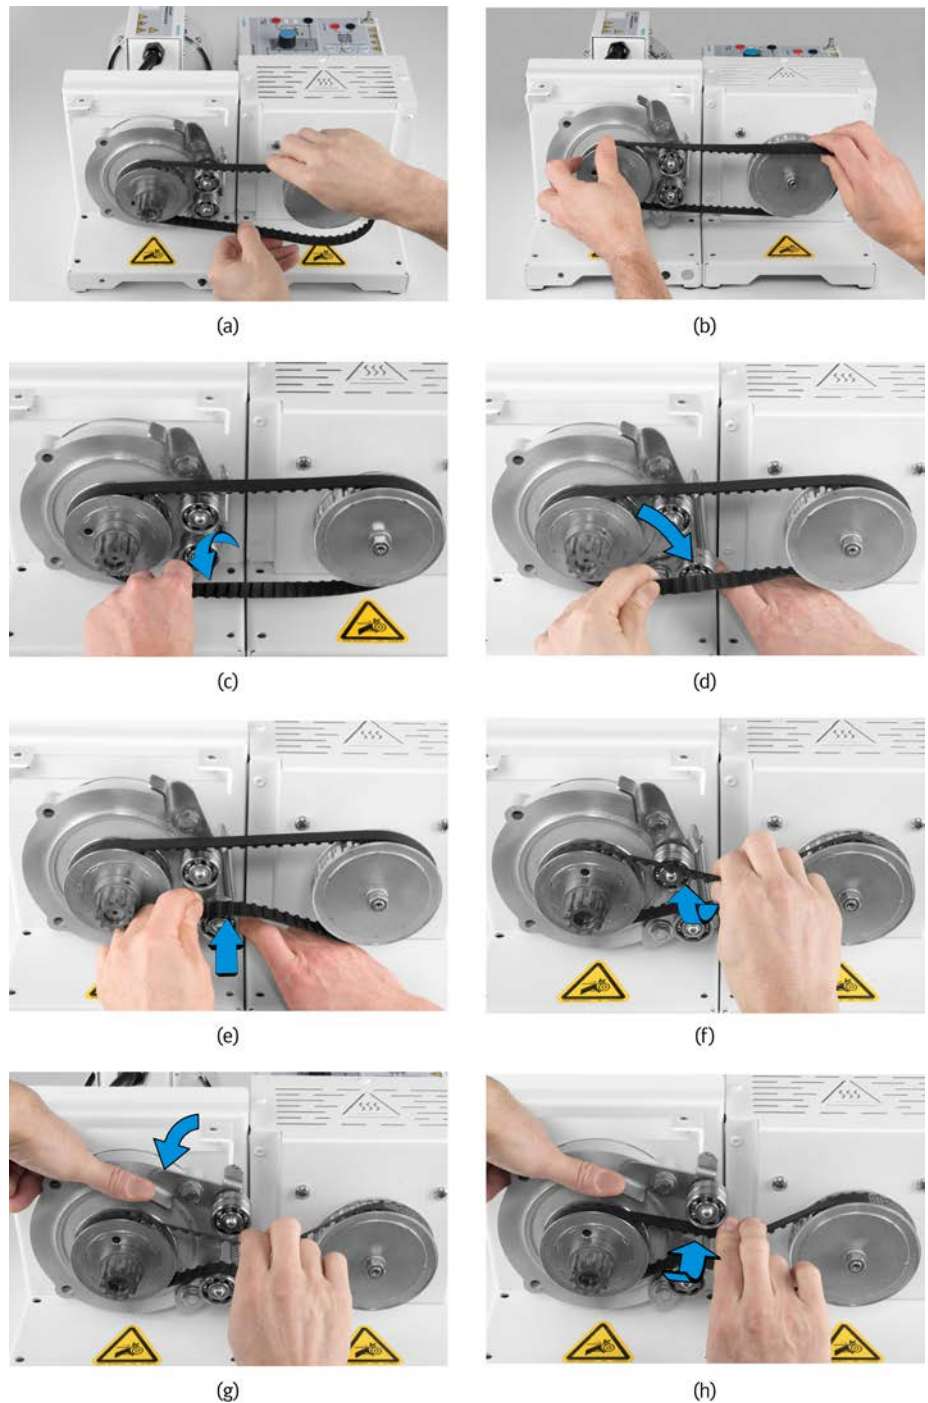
Couplage mécanique d'une machine tournante à la machine motrice à l'aide d'une courroie synchrone.
